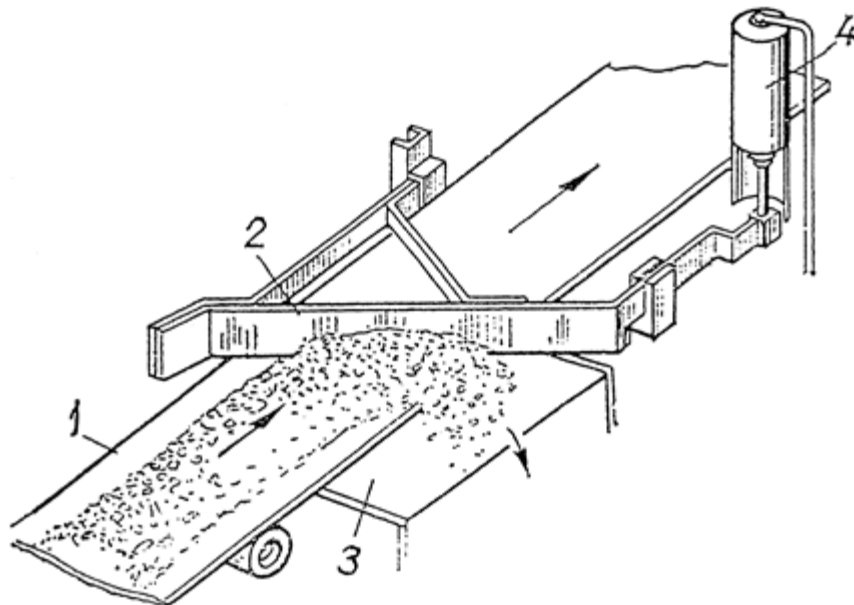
Плужковий розвантажувач: 1 – стрічка; 2 – плужок; 3 – опорний стіл; 4 – підйомний механізм.
